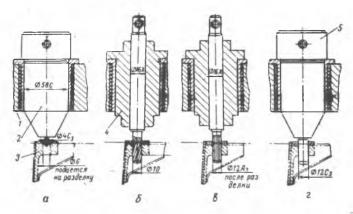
Схема переходов при разделке стыковых отверстий в шпангоуте фюзеляжа: а - предварительный контроль; б - зенкерование; в - развертывание; г - окончательный контроль отверстий:
